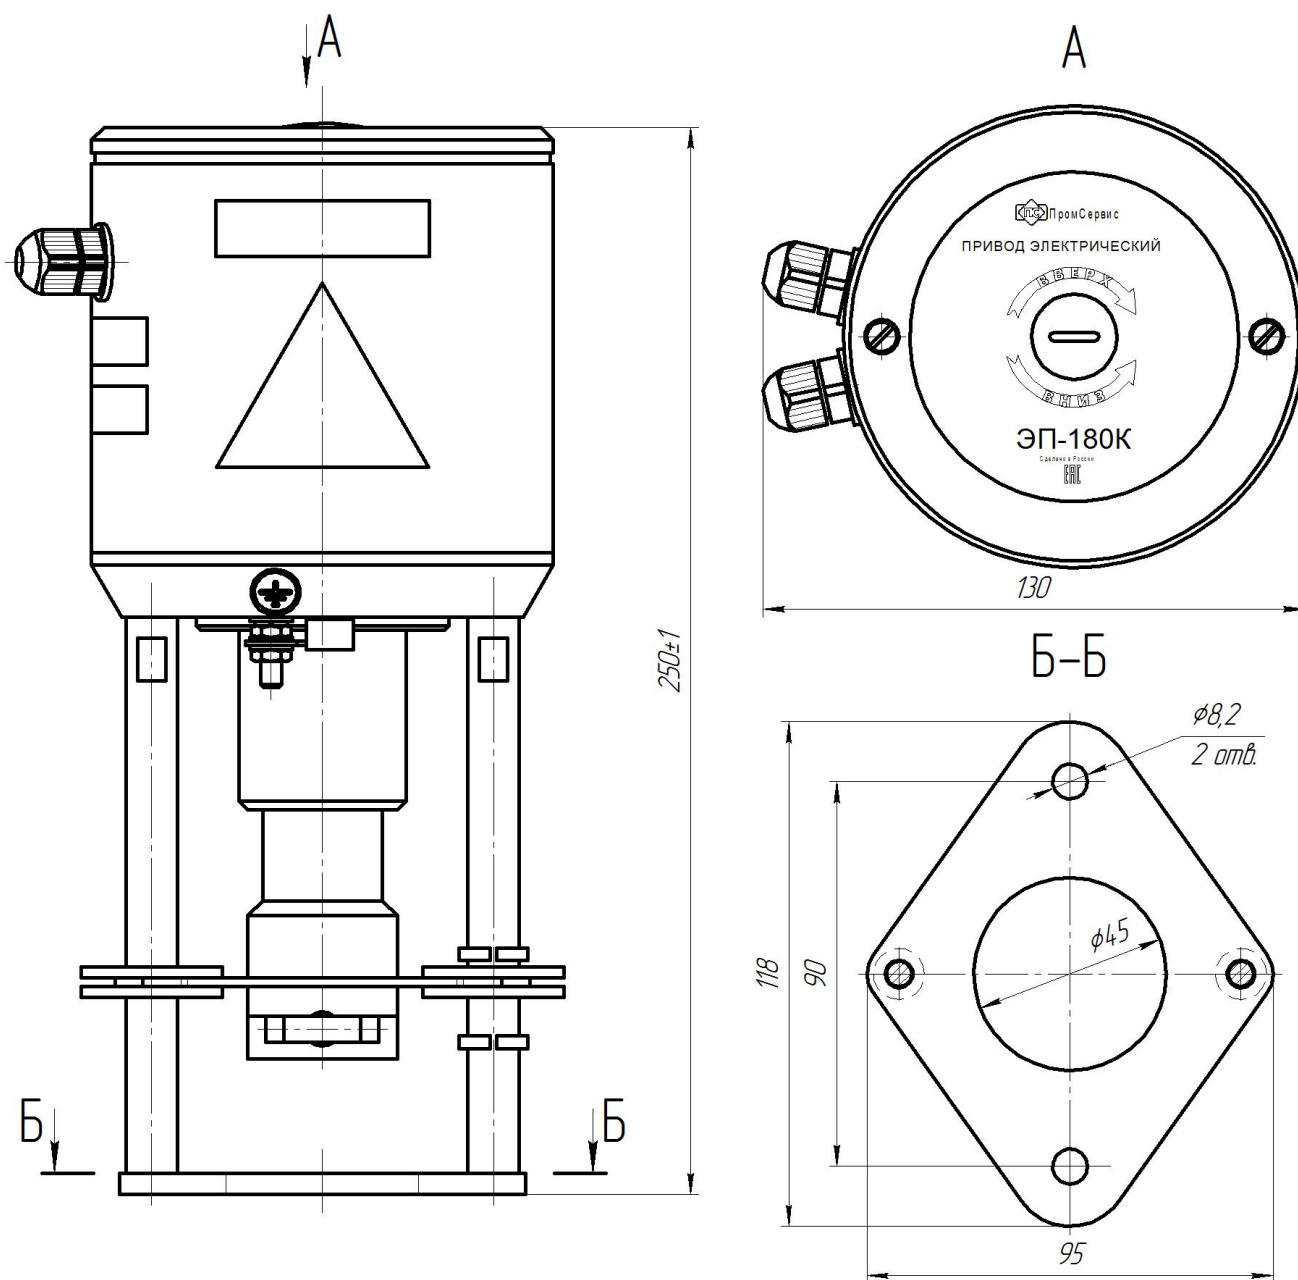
Габаритные и присоединительные размеры привода исполнения ЭП-180К
